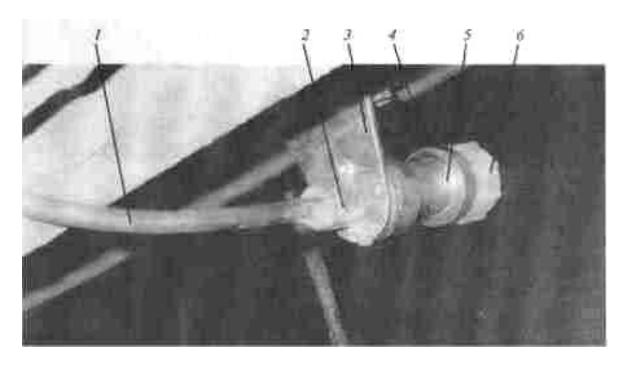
Монтаж и проверка герметичности заправочного устройства: 1- трубопровод; 2- накидная гайка (омылена); 3- кронштейн; 4- бампер; 5- корпус заправочного устройства; 6- защитный колпачок.
